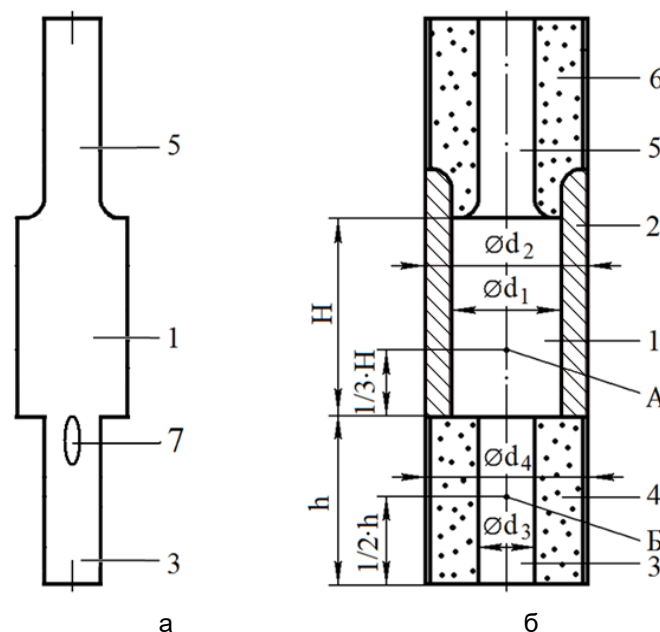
Схема розташування усадкової раковини в нижній шийці валка (а) і основні елементи ливарної форми (б): 1 – бочка валка; 2 – кокіль; 3 – нижня шийка валка; 4 – форма нижній шийки; 5 – верхня шийка; 6 – форма верхній шийки; 7 – усадкова раковина
